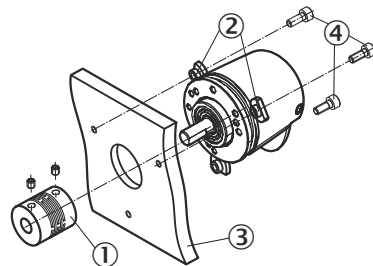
Anbau Klemmflansch mit Servoklammern
